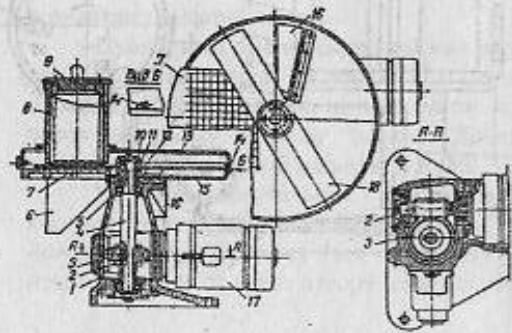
Машини для нарізання варених овочів МРОВ-160: 1 – редуктор черв'ячний; 2 – черв'як; 3 – колесо черв'ячне; 4 – вал вихідний; 5 – підшипники кочення; 6 – лоток розвантажувальний; 7 – ножова решітка; 8 – циліндр завантажувальний; 9 – вантаж-штовхач; 10 – гайка фасонна; 11, 12 – втулки; 13 – кришка; 14 – штифт; 15 – тарілка; 16 – лоток для видалення крихти; 17 – електродвигун; 18 – ніж прямолінійний
